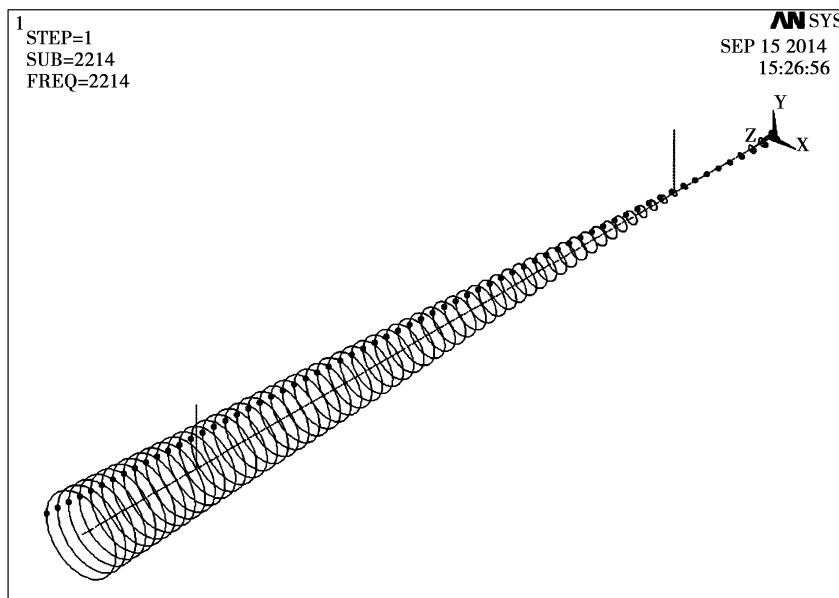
高速 PCB 钻削电主轴转子-支承系统简化模型
